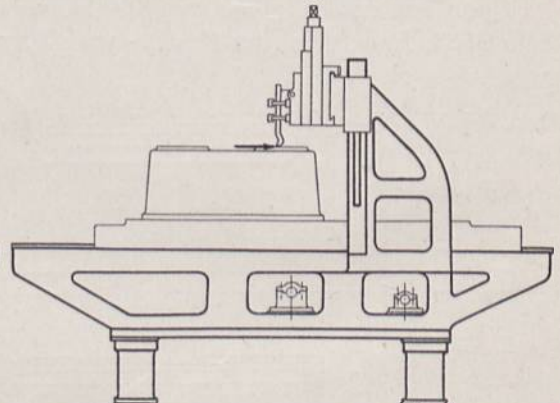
Hobelmaschinenrahmen älterer Form.
